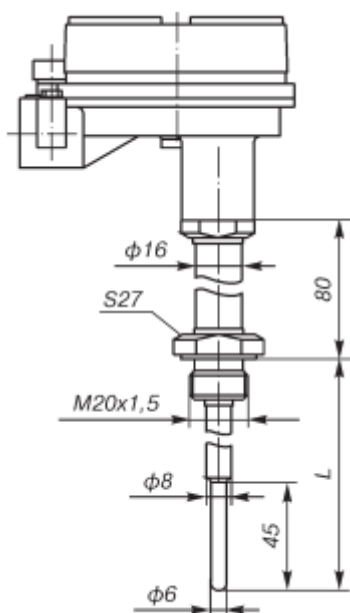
Габаритные и присоединительные размеры Метран-276
